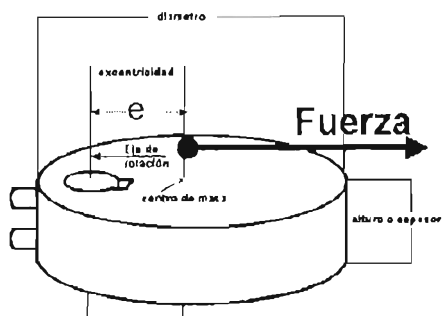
Masa excéntrica diseñada para el vibrador circular.
